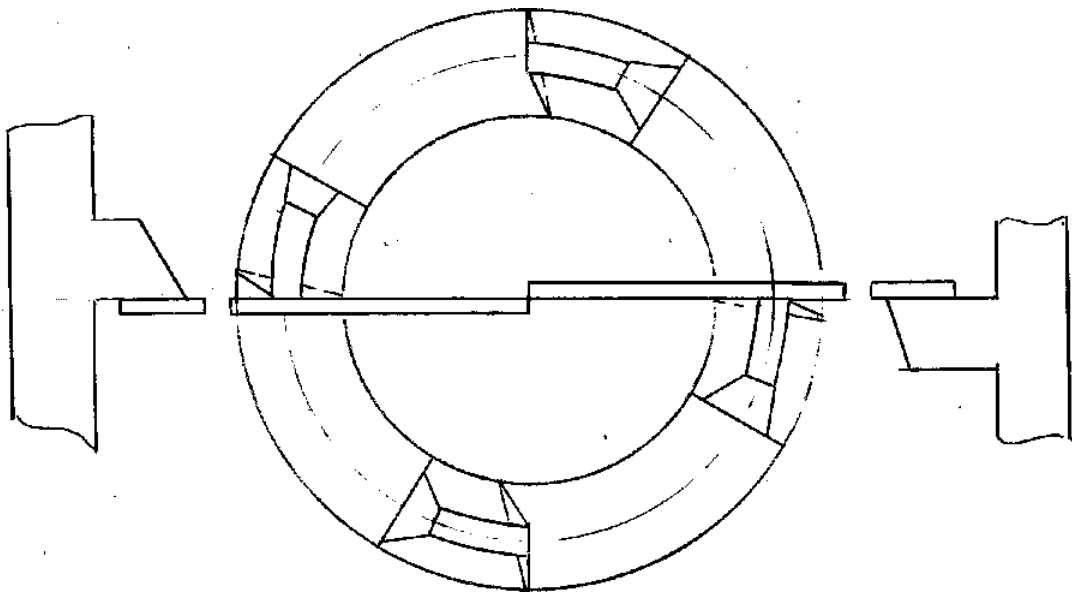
линейка для измерения положения режущих кромок резцов.
